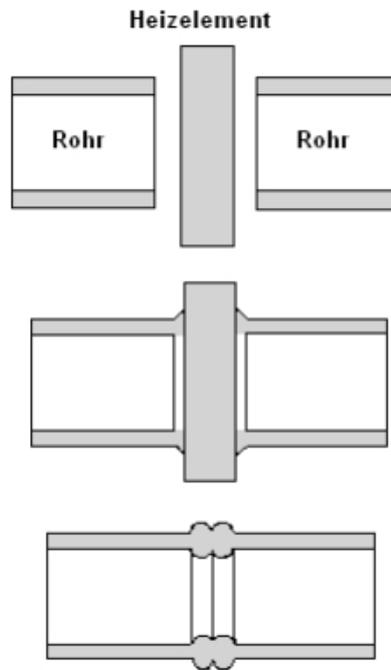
Heizelement-Stumpfschweißen⁸⁴
